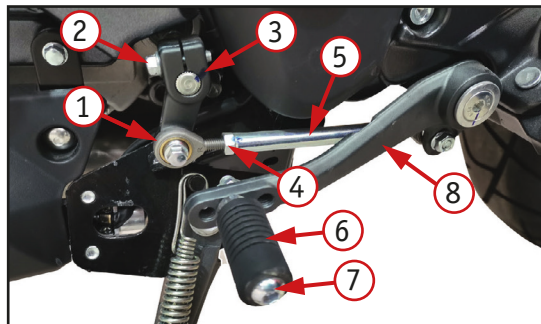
Регулировка рычага переключения передач: 1– наконечник штока; 2– крепежный болт; 3– шатун передач; 4– стопорная гайка; 5– шток; 6– лапка рычага переключения передач; 7– болт крепления лапки; 8– рычаг.
